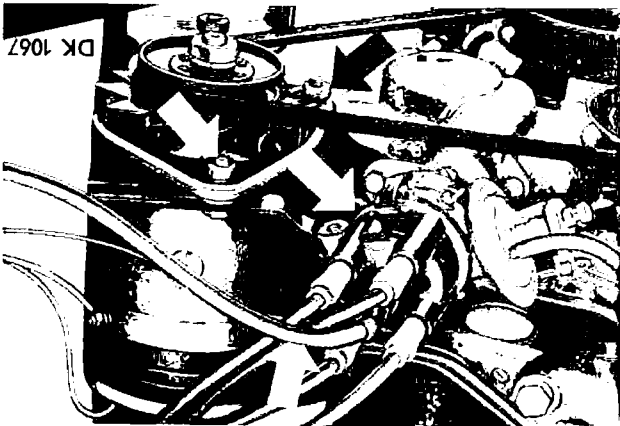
/5 Befestigungsschrauben der Lichtmaschine
